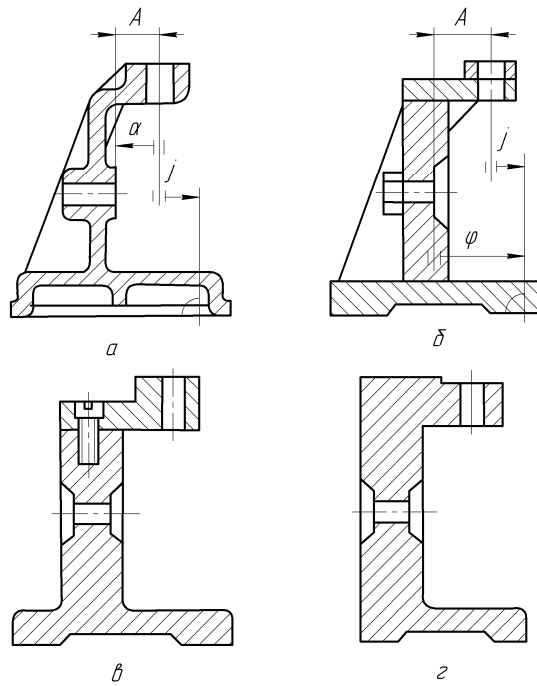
Різні типи корпусу пристрою в розрізі: *а* – литий; *б* – зварний; *в* – збірний; *г* – кутовий (після зняття напусків і припусків)
